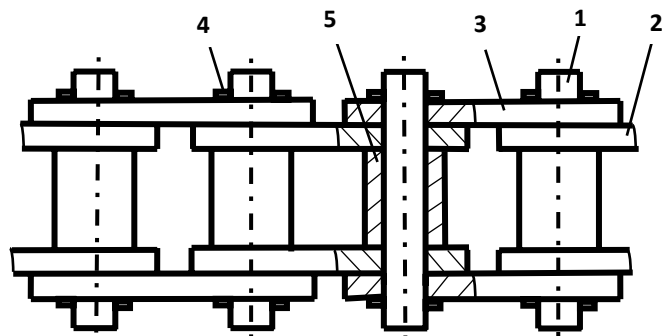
Фрагмент приводной пластинчатой цепи [10] с гладкими валиками и дистанционными втулками
